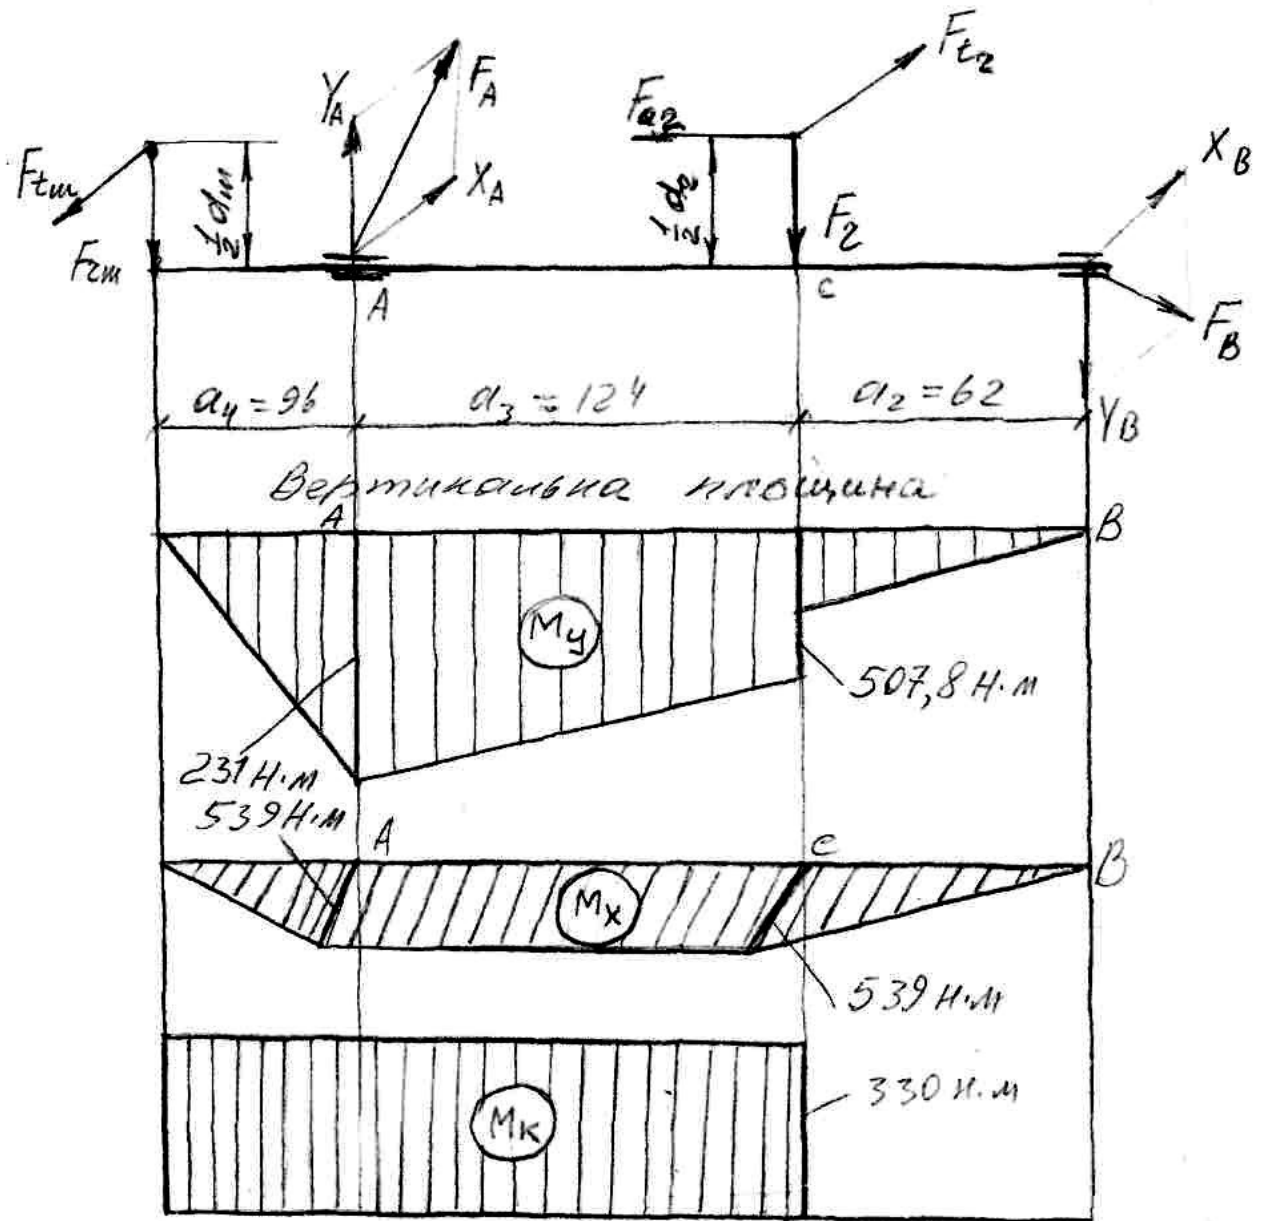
Розрахункова схема вала черв'ячного колеса
